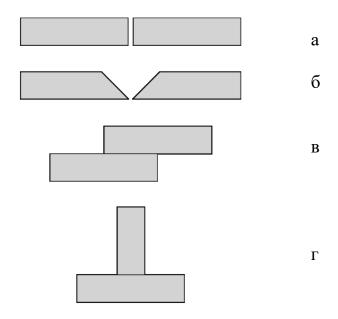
Типы сварных соединений: а – стыковые без разделки кромок, б – стыковые с разделкой кромок, в – нахлесточные, г – тавровые
